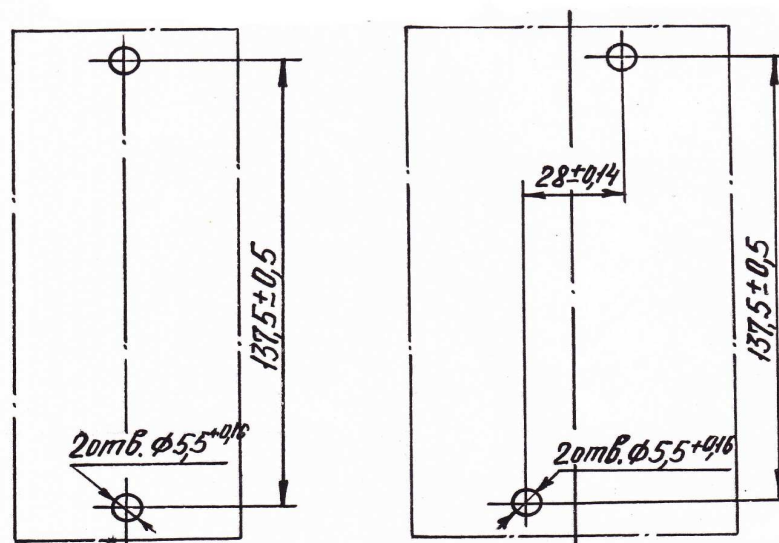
Сверление отверстий под винты крепления двухполюсного и трехполюсного выключателей
